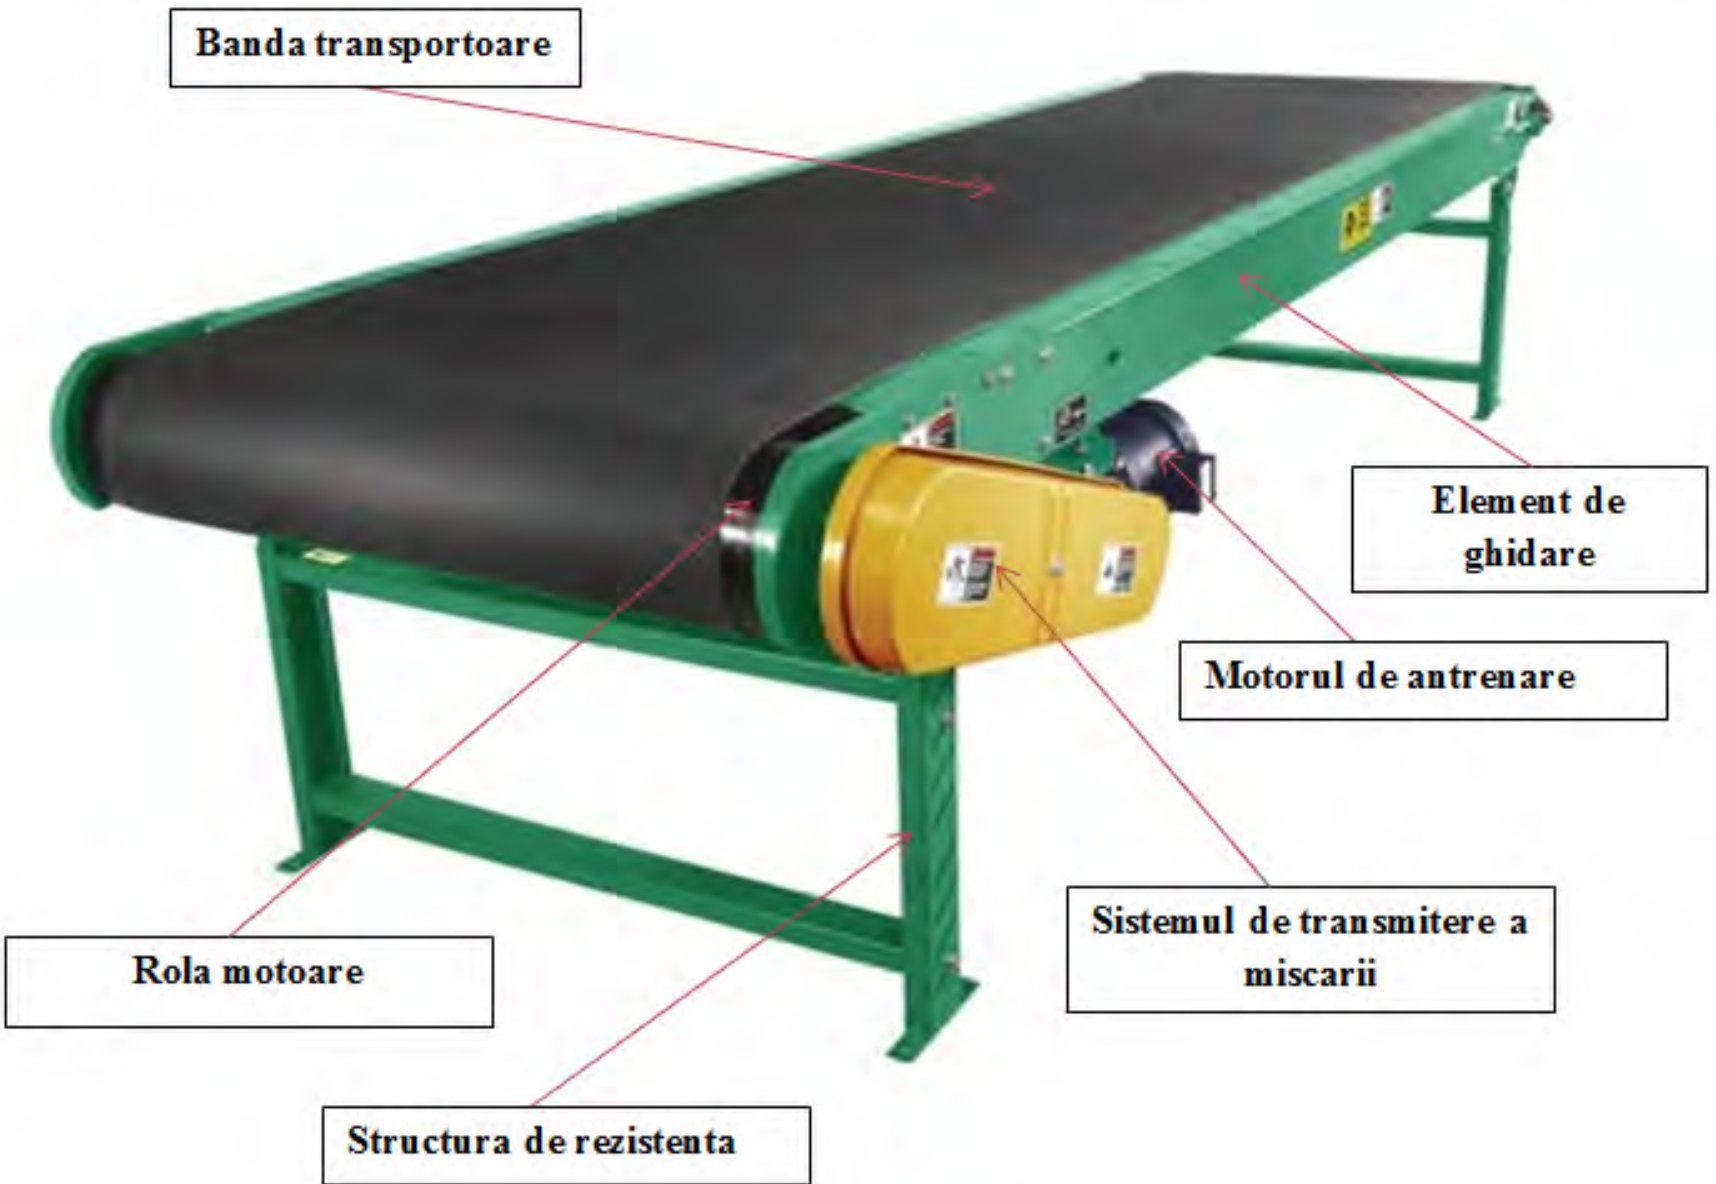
Conveier cu banda dublă - elemente constructive de bază
